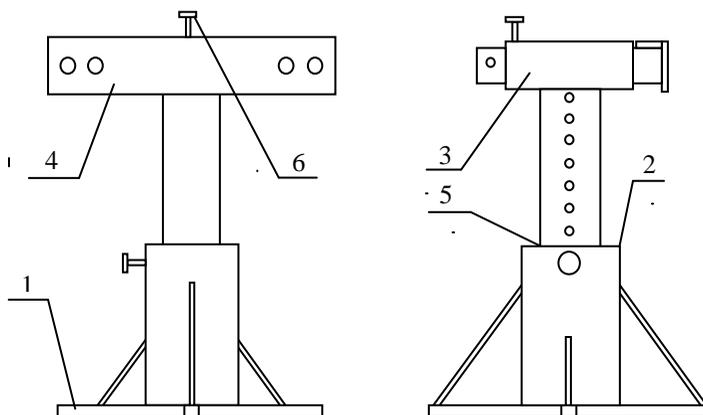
Стойка кантователя несущего кузова легкового автомобиля: а – вид спереди; б – вид сбоку; 1 – основание; 2 – направляющая стойка; 3 – регулировочная опора; 4 – поворотная планка; 5 – фиксатор регулировочной опоры; 6 – фиксатор поворотной планки
